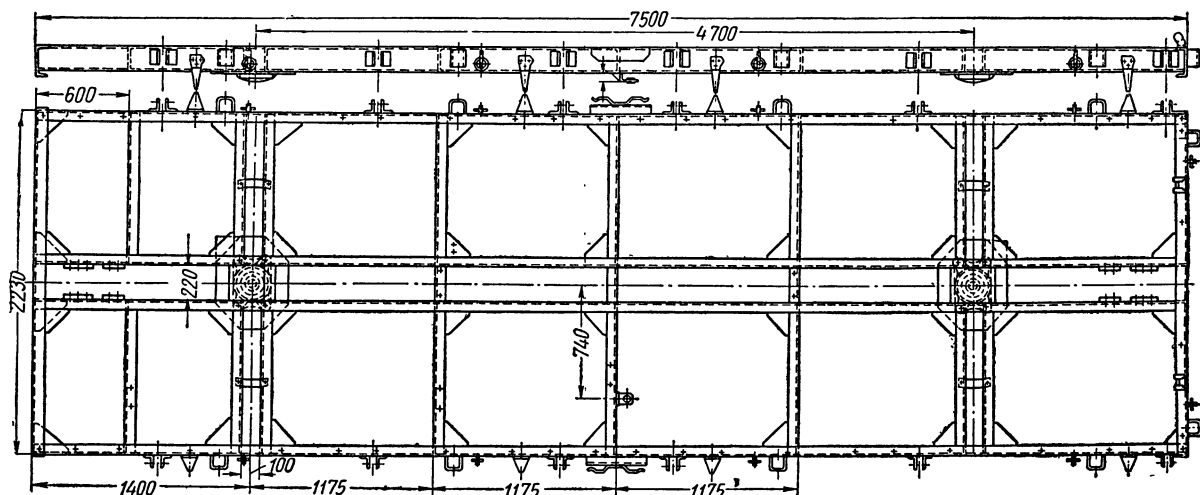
Рама сварная четырехосного 60-тонного вагона-самосвала.
